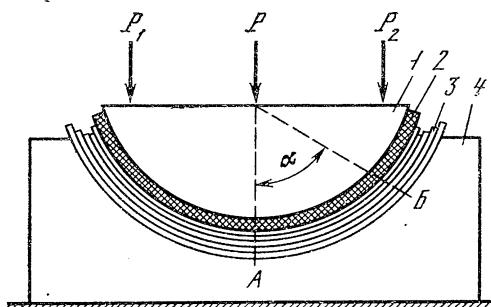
Схема склеивания заготовок незамкнутого контура из планок в жесткой пресс-форме:
